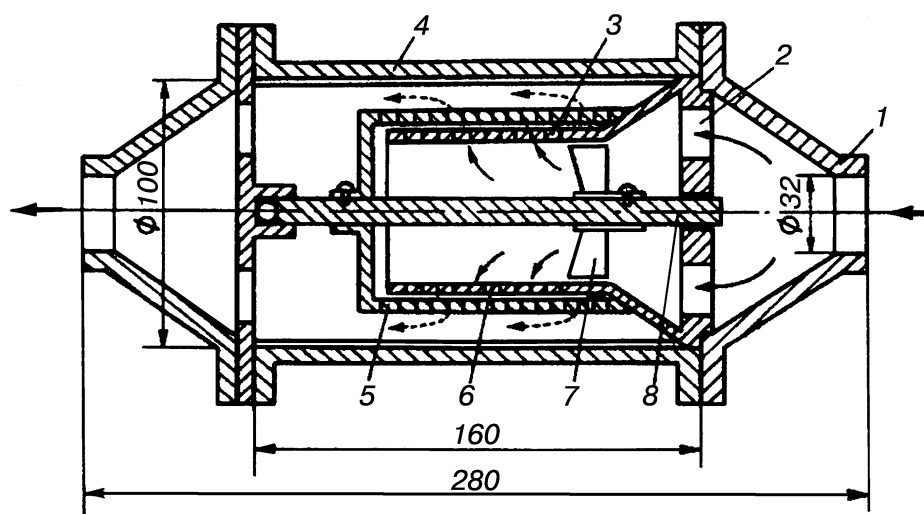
Роторный эмульсатор: 1 – патрубок; 2 – перегородка с распределенными отверстиями; 3 – неподвижный цилиндр-статор; 4 – корпус; 5 – радиальные отверстия; 6 – вращающийся цилиндр-ротор; 7 – турбинка; 8 – вал
